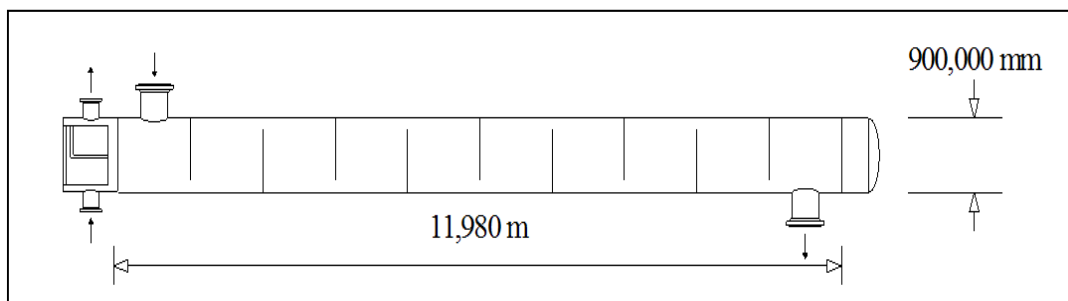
Dimensiones generales Sobrecalentador. Fuente: HTRI Output drawing.
